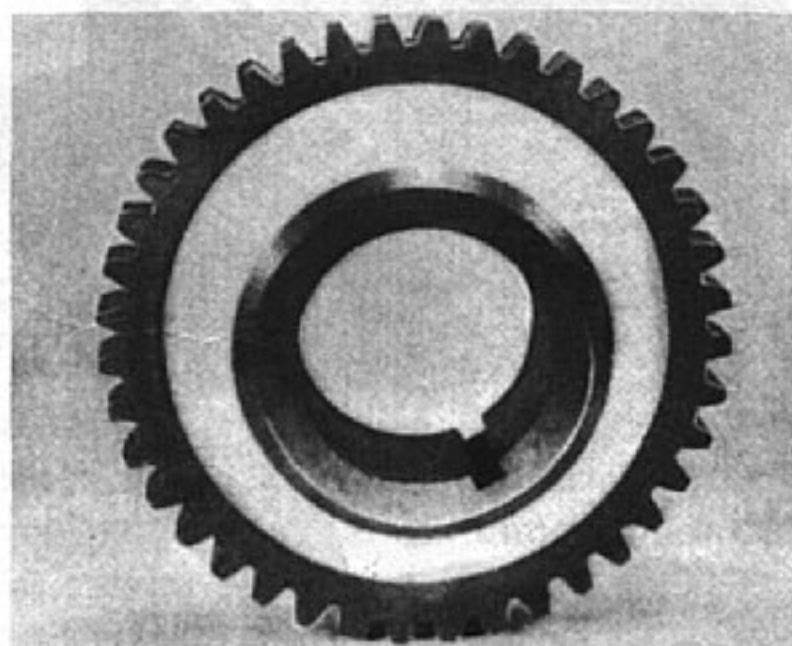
Rueda cilíndrica de dientes rectos. (The Fellows Gear Shaper Company.)
